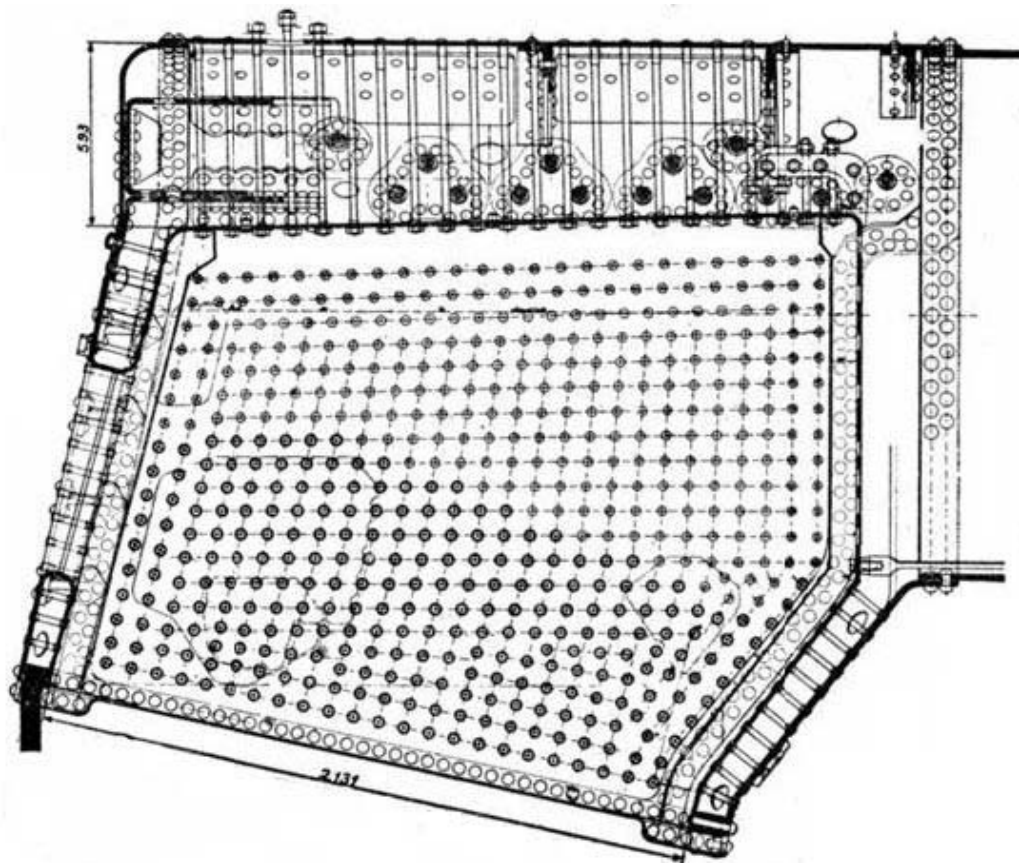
Caja de fuego y hogar en acero de las locomotoras 141 P; corte longitudinal. Caras anterior y posterior inclinadas; chapas soldadas con autógena en torno a la apertura de la puerta.
